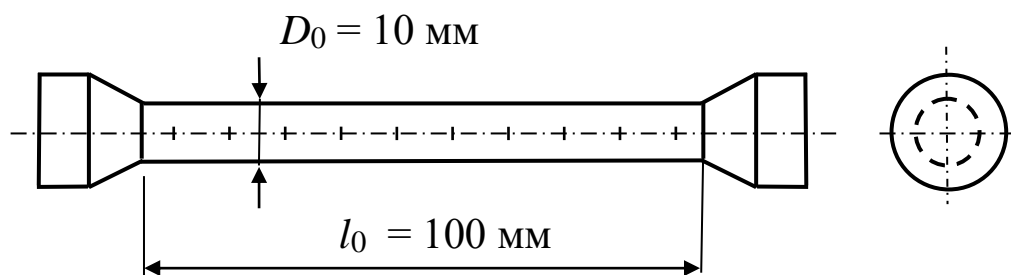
Схема образца для испытаний стали на растяжение
